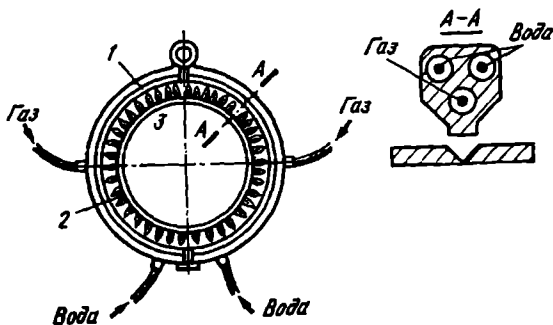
Горелка для газопрессовой сварки труб:
